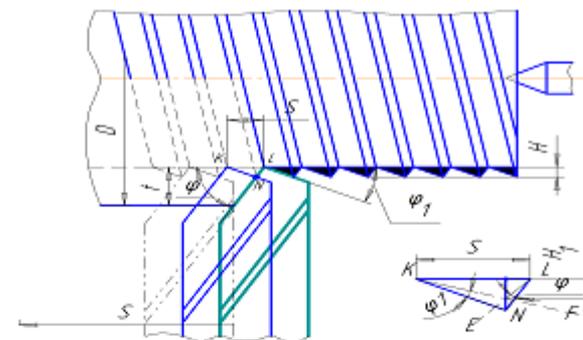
Профиль обработанной поверхности при резании резцом с  $r=0$
